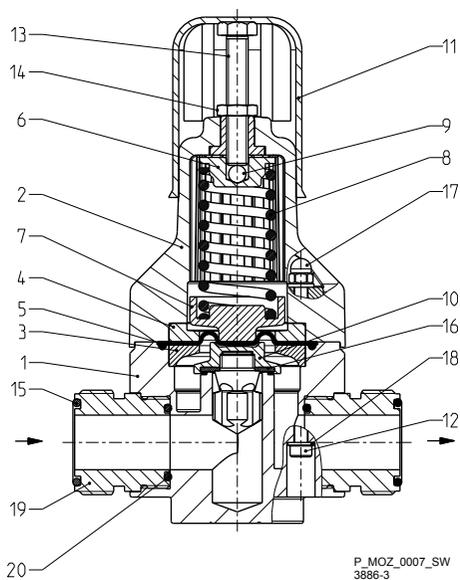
Vista in sezione DHV-U PVC, PP, PVDF
